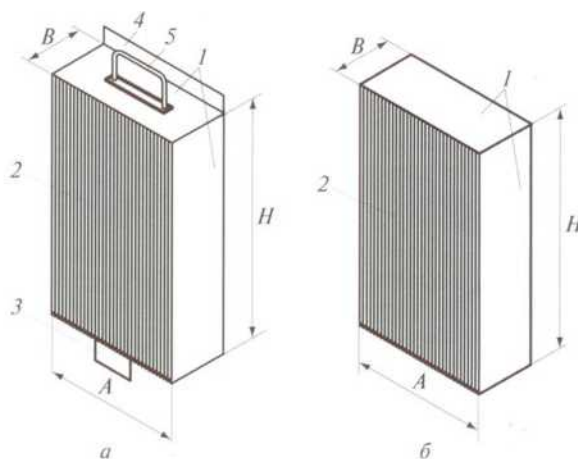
Конструкция жалюзийного съёмного пакета: а – исполнение 1; б – исполнение 2
